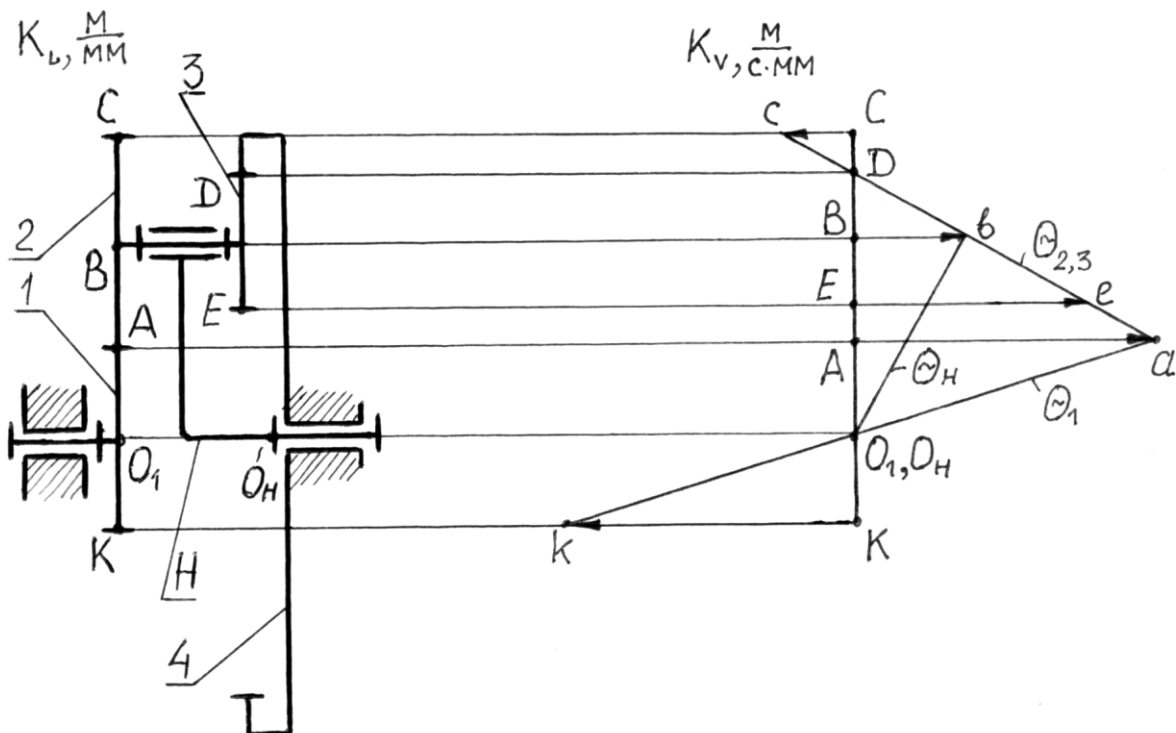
Кинематическая схема и план скоростей планетарного механизма.
